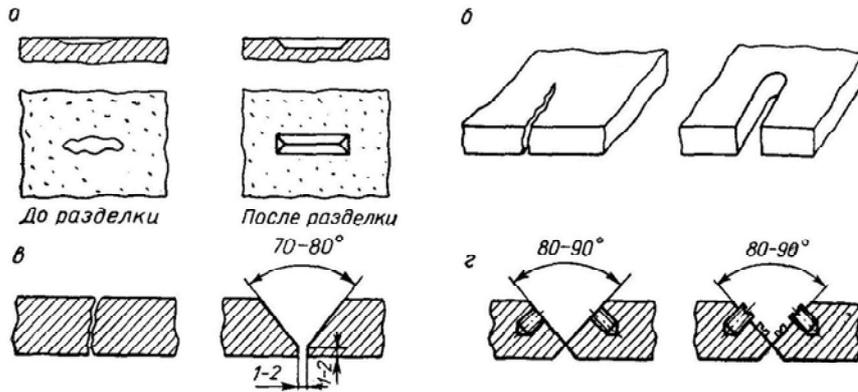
Схема подготовки дефекта к сварке:
